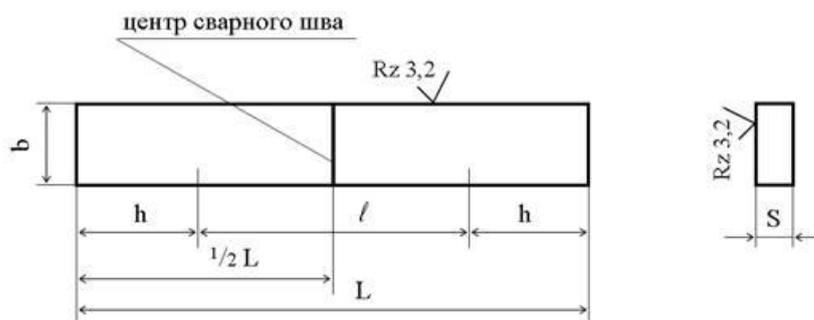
Форма образца: (тип XII) для испытаний сварного соединения на статическое растяжение
